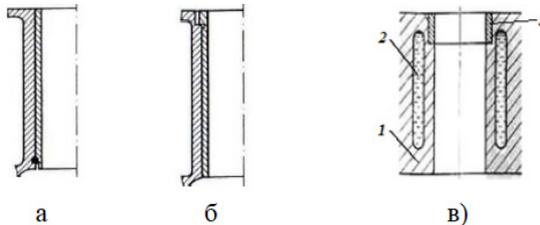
«Сухие» гильзы цилиндров: а) без опорного бурта; б) с верхним опорным буртом; в) с короткой вставкой: 1 – блок цилиндров; 2 – водяная рубашка; 3 – вставка
